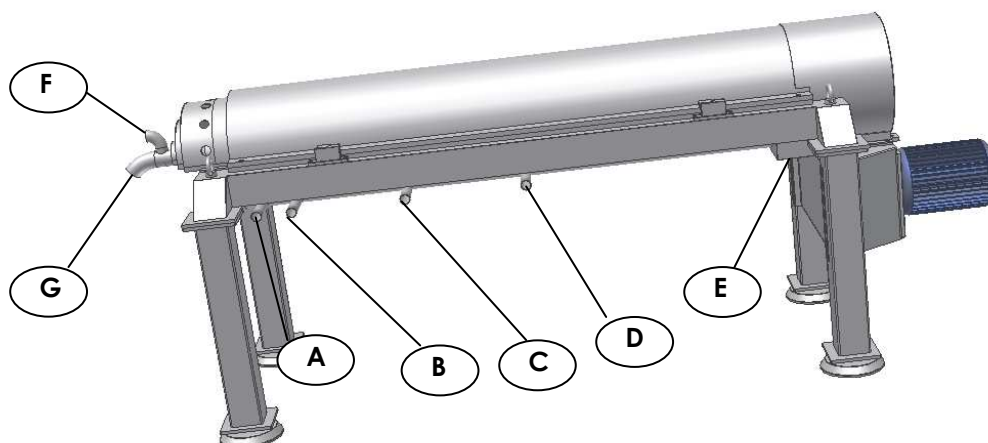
Collegamenti idraulici / Hydraulic connections
